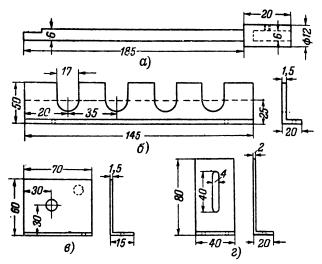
Основные крепящие детали. α — удлиненная ось к переключателю диапазонов; δ — подставка для электролитических конденсаторов фильтра; ϵ — стойка для крепления переключателя диапазонов; ϵ — стойка для крепления кинескопа (2 шт.).
